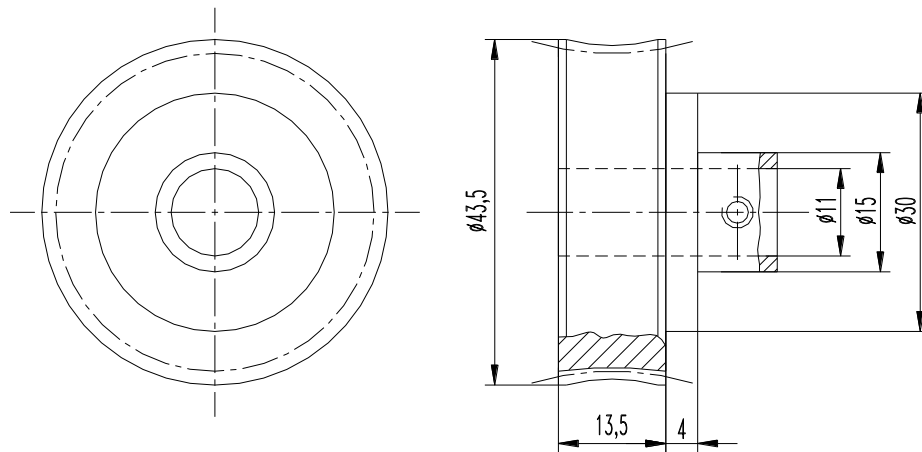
Dimensiones de Rueda dentada para tornillo sin-fin
